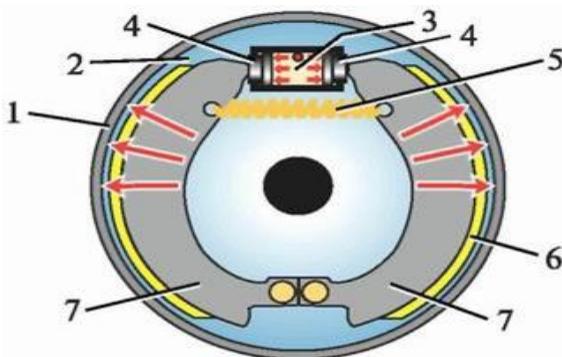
Схема работы барабанного тормозного механизма: 1 – тормозной барабан; 2 – тормозной щит; 3 – рабочий тормозной цилиндр; 4 – поршни рабочего тормозного цилиндра; 5 – стяжная пружина; 6 – фрикционные накладки; 7 – тормозные колодки
